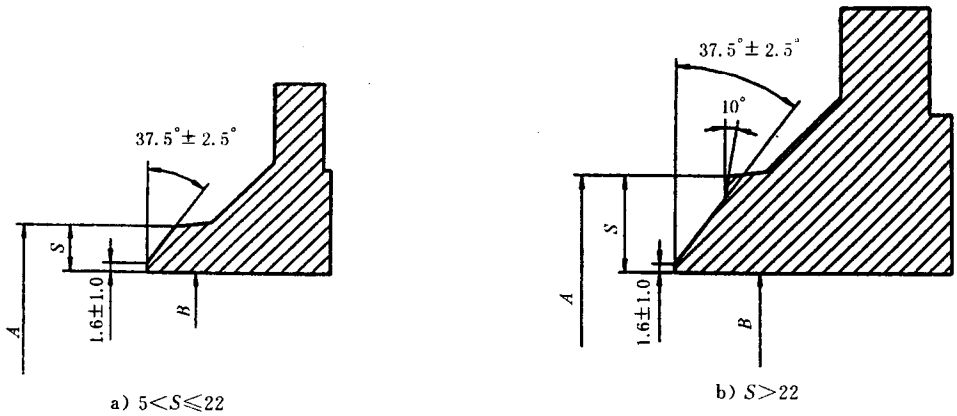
带颈承插焊法兰与钢管连接的焊接接头型式
